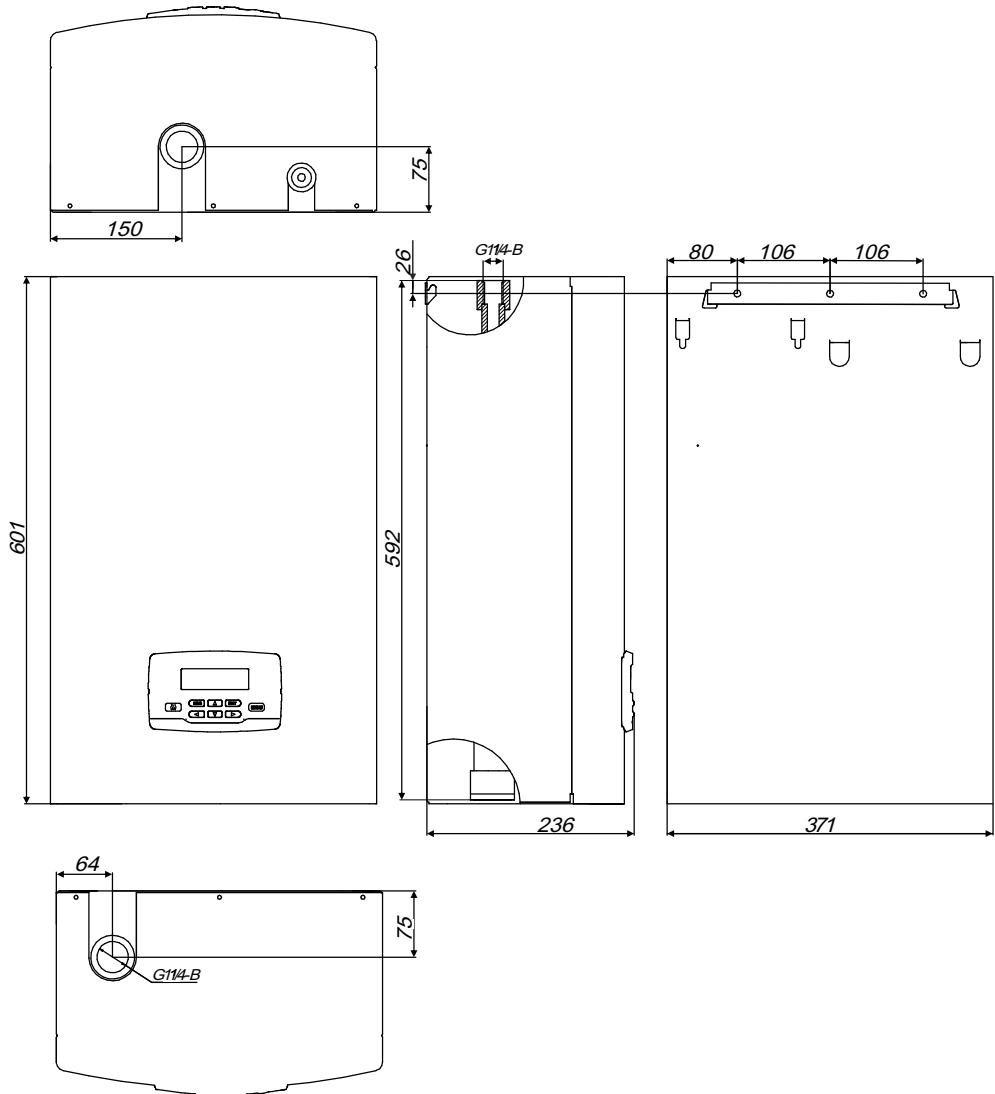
Габаритные и присоединительные размеры прибора ЭВАН PRACTIC -3 ... -28
